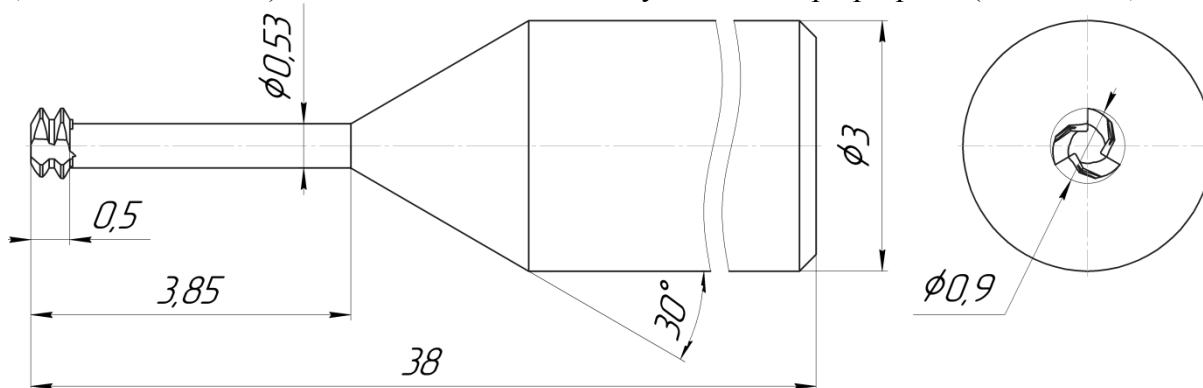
Резьбовая фреза для обработки резьбы М1,2х0,25.
